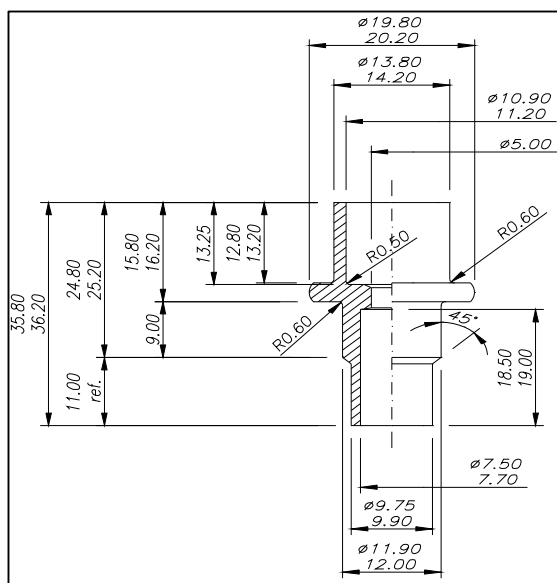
Dimensão final do produto na usinagem após operação de torneamento e furação
